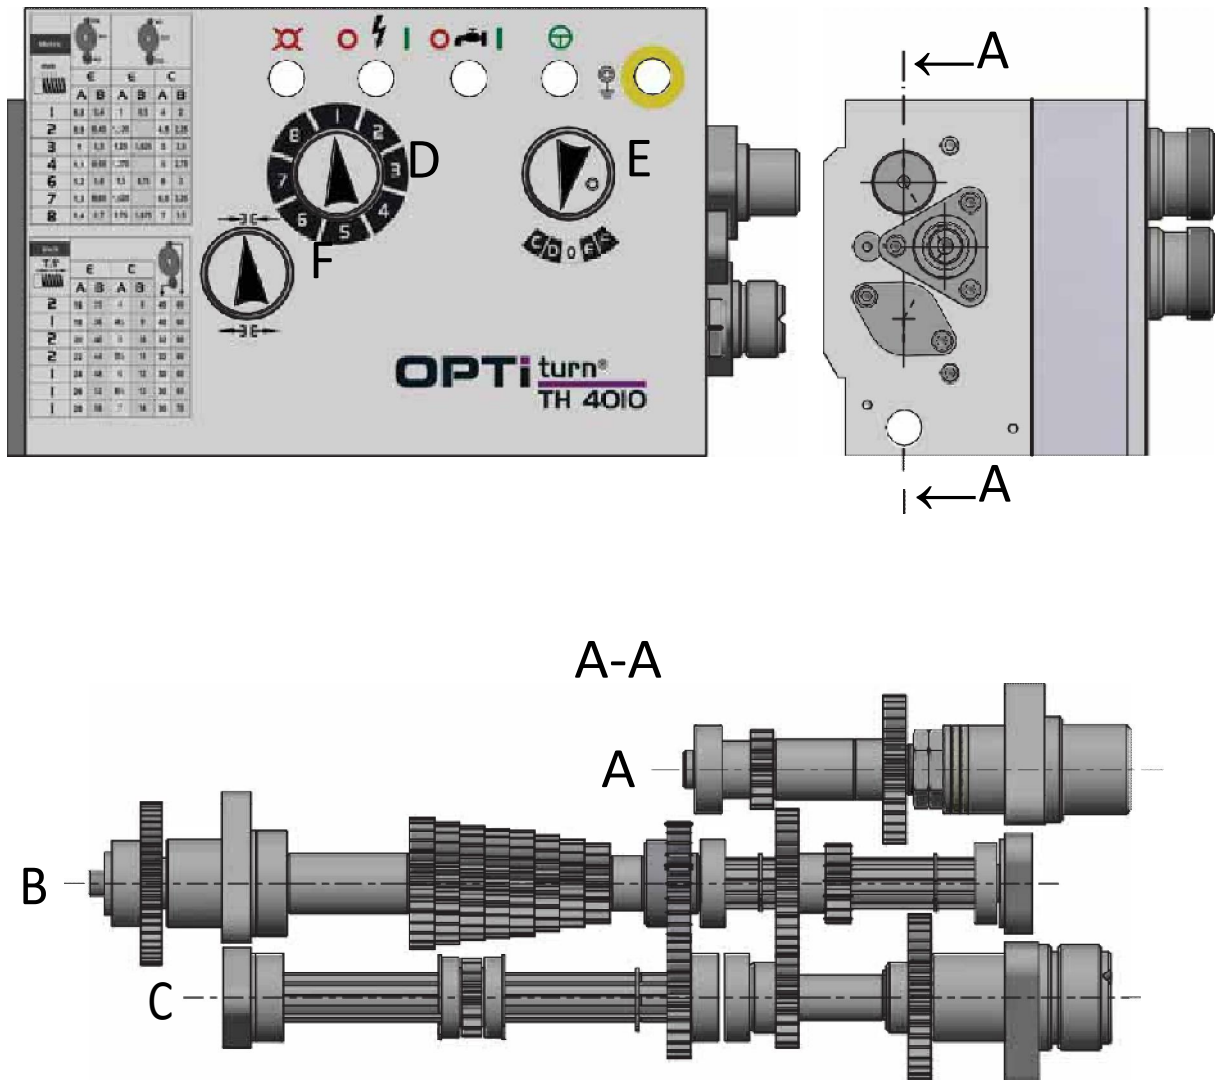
Vorschubgetriebe –Engranaje de avance
